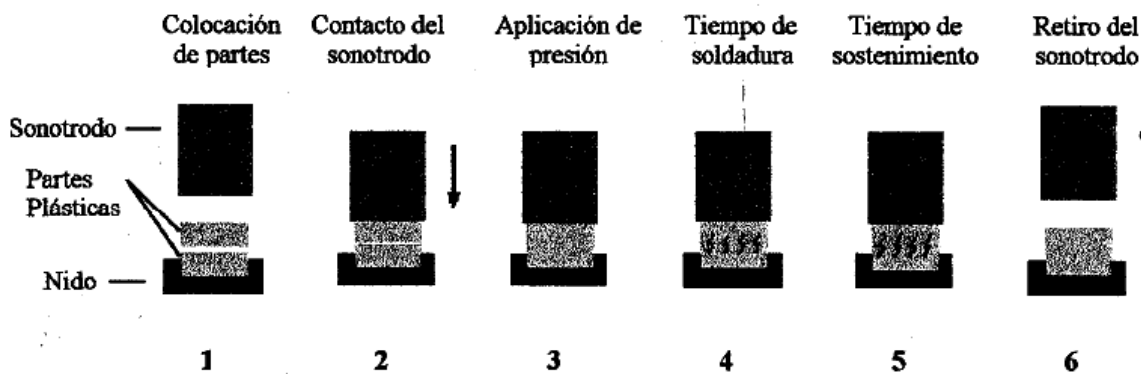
Etapes de la soldadura per ultrasons
